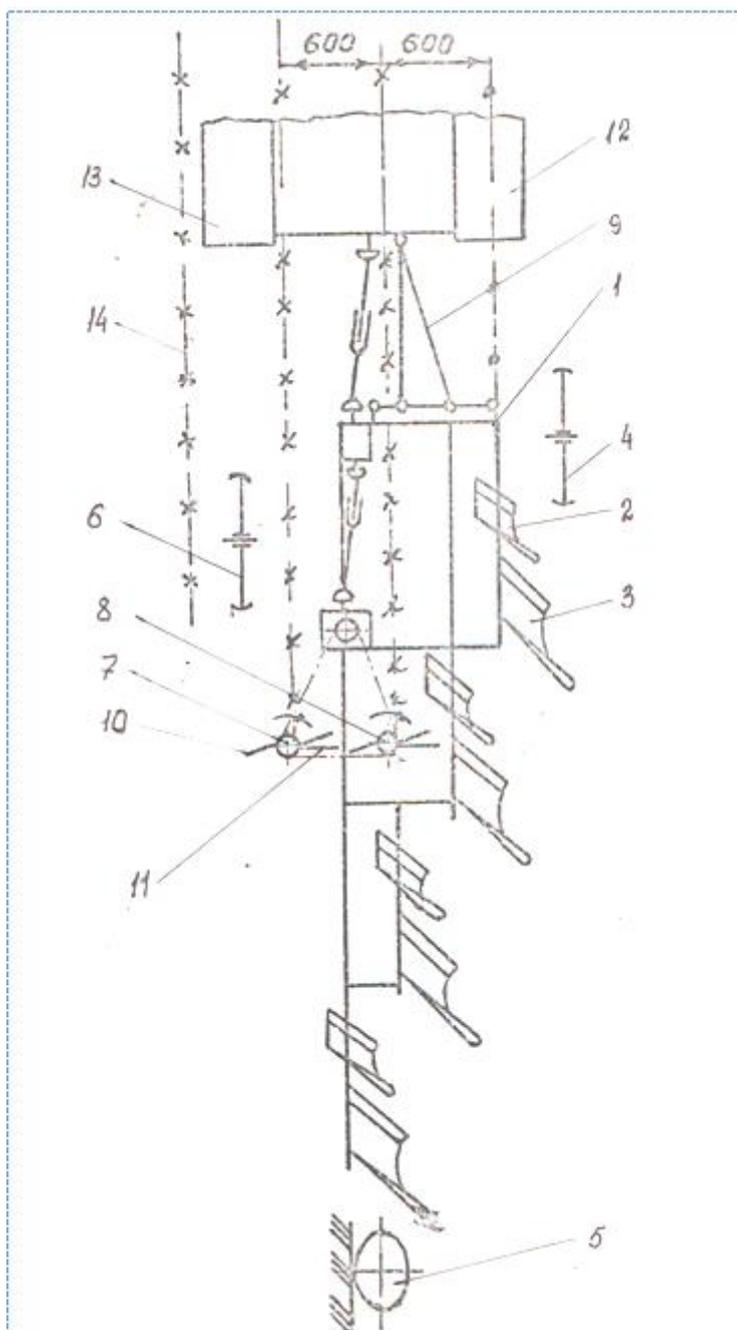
Конструктивно - технологическая схема комбинированного двухъярусного плуга ПЯ-4-30 (вид сверху)
